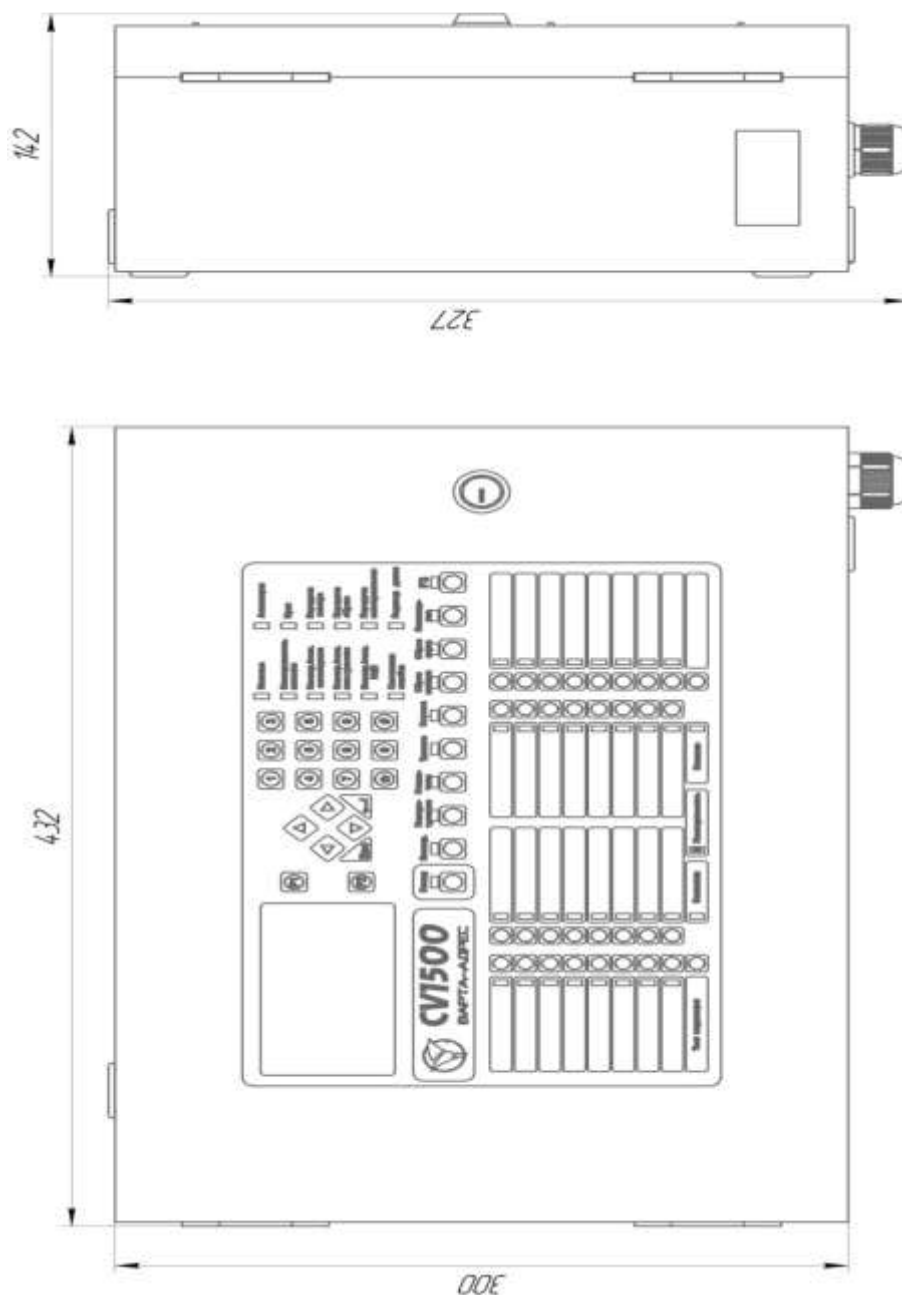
Общий вид и габаритные размеры ППКП-А
